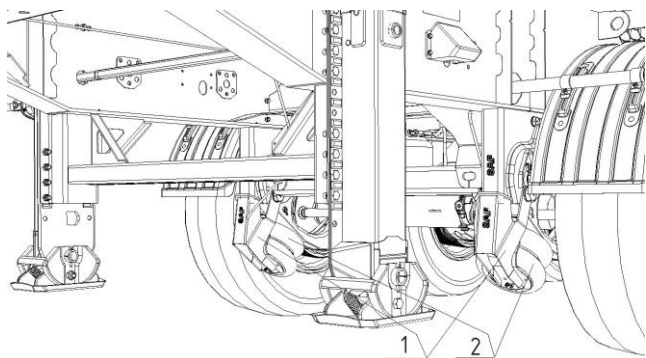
Двухсторонний механизм подъёма оси с пневмоподушкой.
